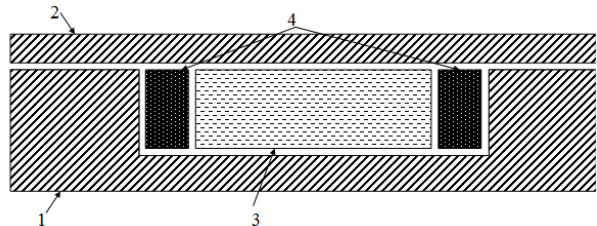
(1 – металлический корпус с выфрезерованной полостью, 2 – металлическая крышка, 3 – фторопластовая пластина, 4 – СВЧ-поглотители мощности)
